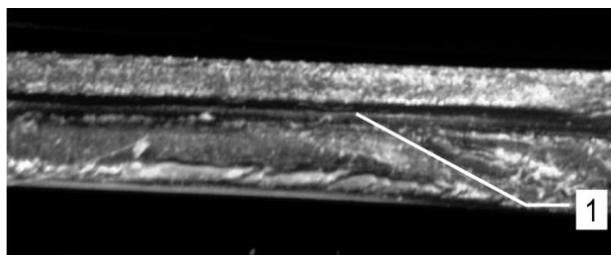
Стадия обеспечения акустического контакта между сварочным инструментом и материалами
